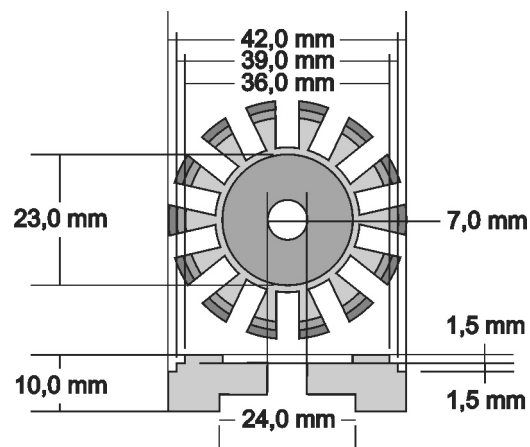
Technische Zeichnung der Basisplattform – der so genannte Rotor.
